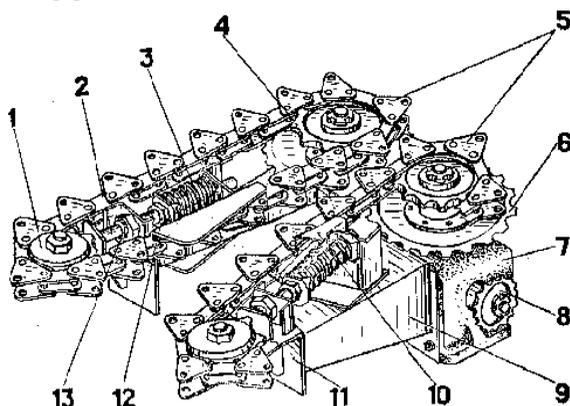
Русло (режущий аппарат): 1 - натяжная звездочка; 2 - винт натяжной; 3 - пружина; 4 - ведущая звездочка; 5 - транспортерная цепь; 6 - нож; 7 - приводная коробка; 8 - полумуфта; 9 - продольная балка рамы; 10 - направляющий кронштейн с ползком; 11 - опорный кронштейн; 12 - гайка; 13 - втулка
